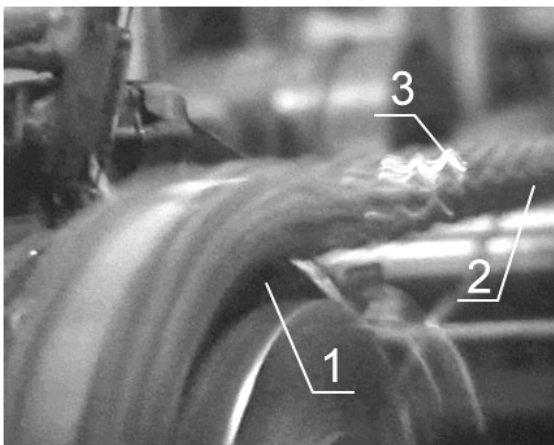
Фото работающей роликовой цепной передачи: 1 – ведомая звездочка; 2 – ведущая ветвь цепи; 3 – траектория движения шарнира
